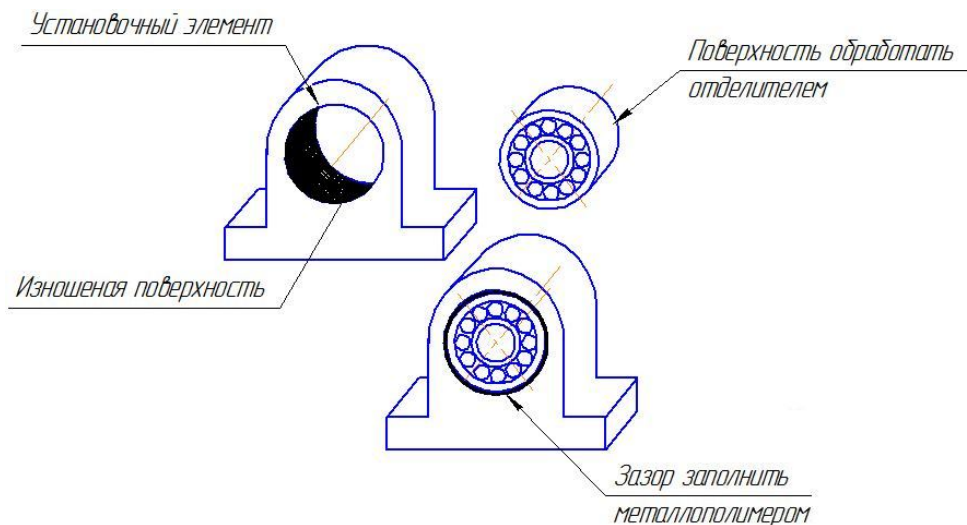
Технология восстановления опорной поверхности неразъёмного корпуса подшипника качения
